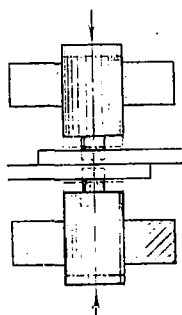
Схема холодной сварки методом пластической деформации.
